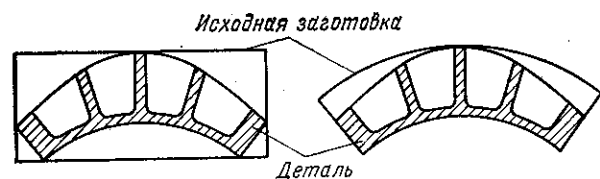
Исходные заготовки для фрезерования панелей криволинейной формы
